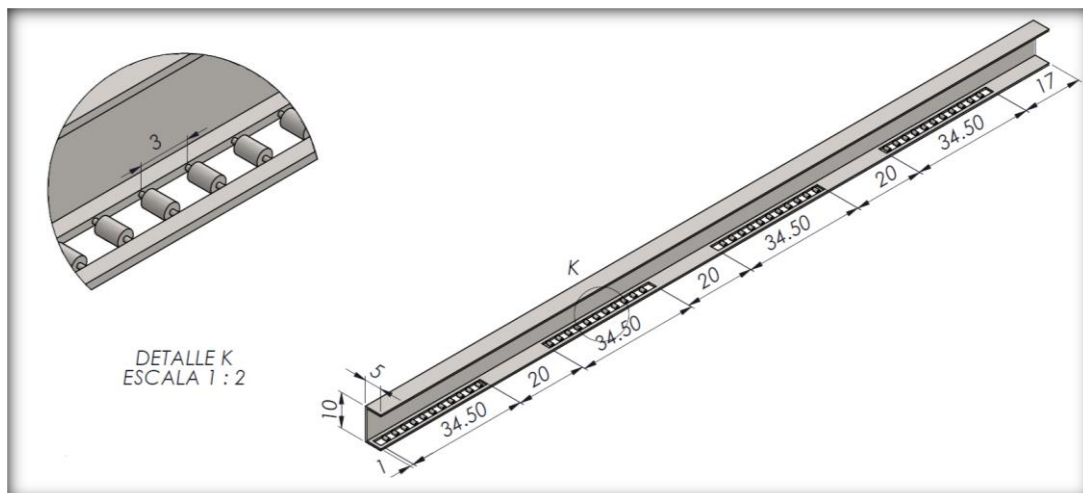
Perfil con rodamientos detallado. Cotas en cm.
